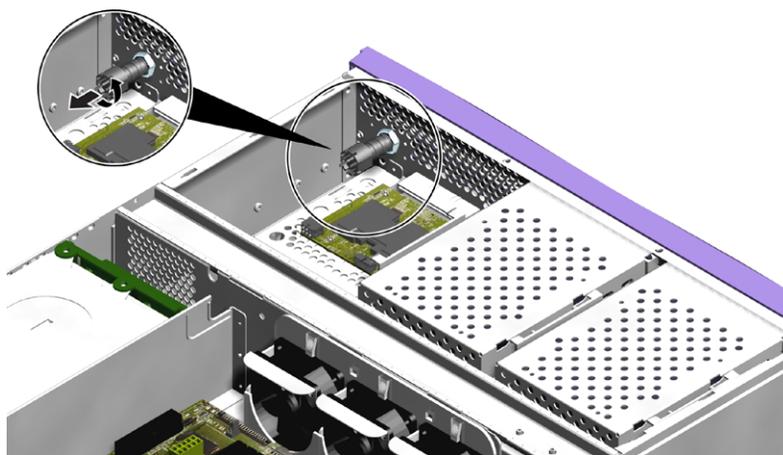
Disconnessione del cablaggio dell'interruttore a chiave
